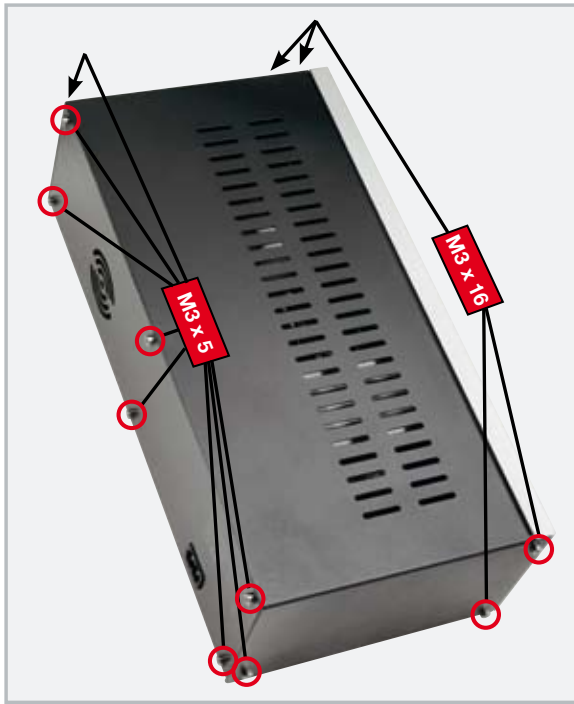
Montage des Gehäusedeckels mit Inbusschrauben
